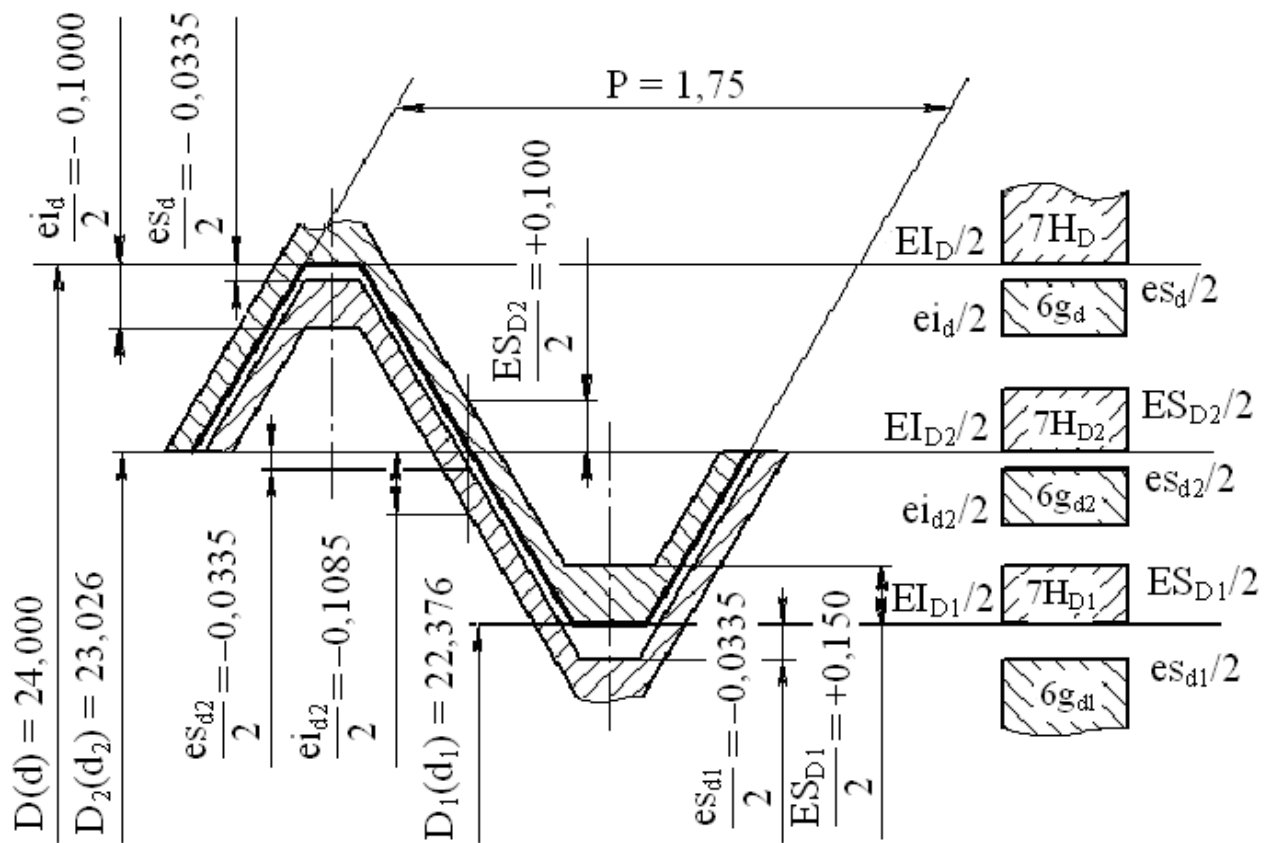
Схема розташування допусків профіля та полів допусків для нарізного з'єднання М12–6Н/6g
